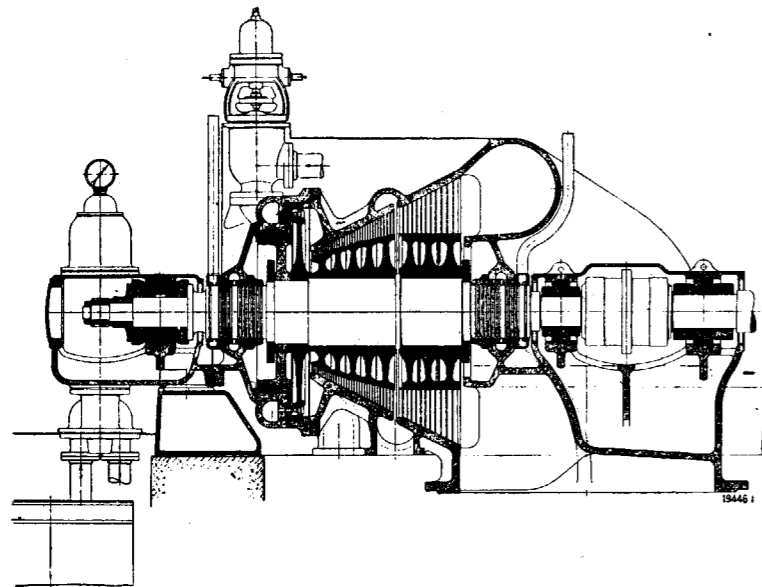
Corte de una turbina monocilíndrica combinada, 10.000 kilovatios, 3.000 revoluciones por minuto.
